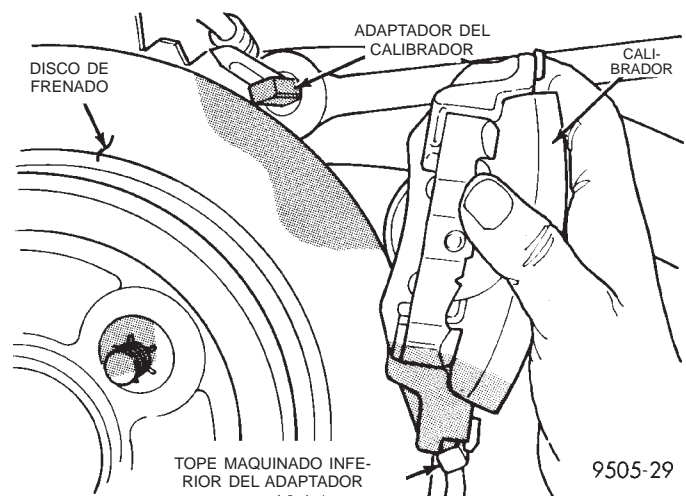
Desmontaje del conjunto de calibrador del adaptador
